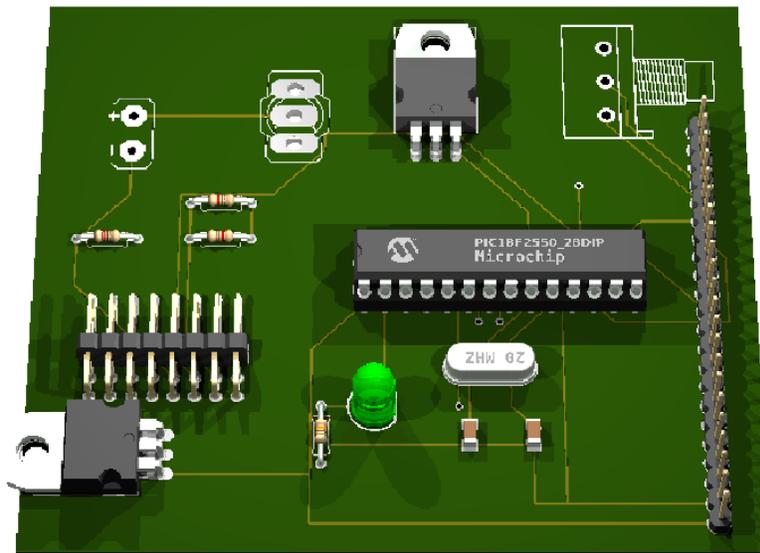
Diseño de la placa del circuito integrado en tercera dimensión
